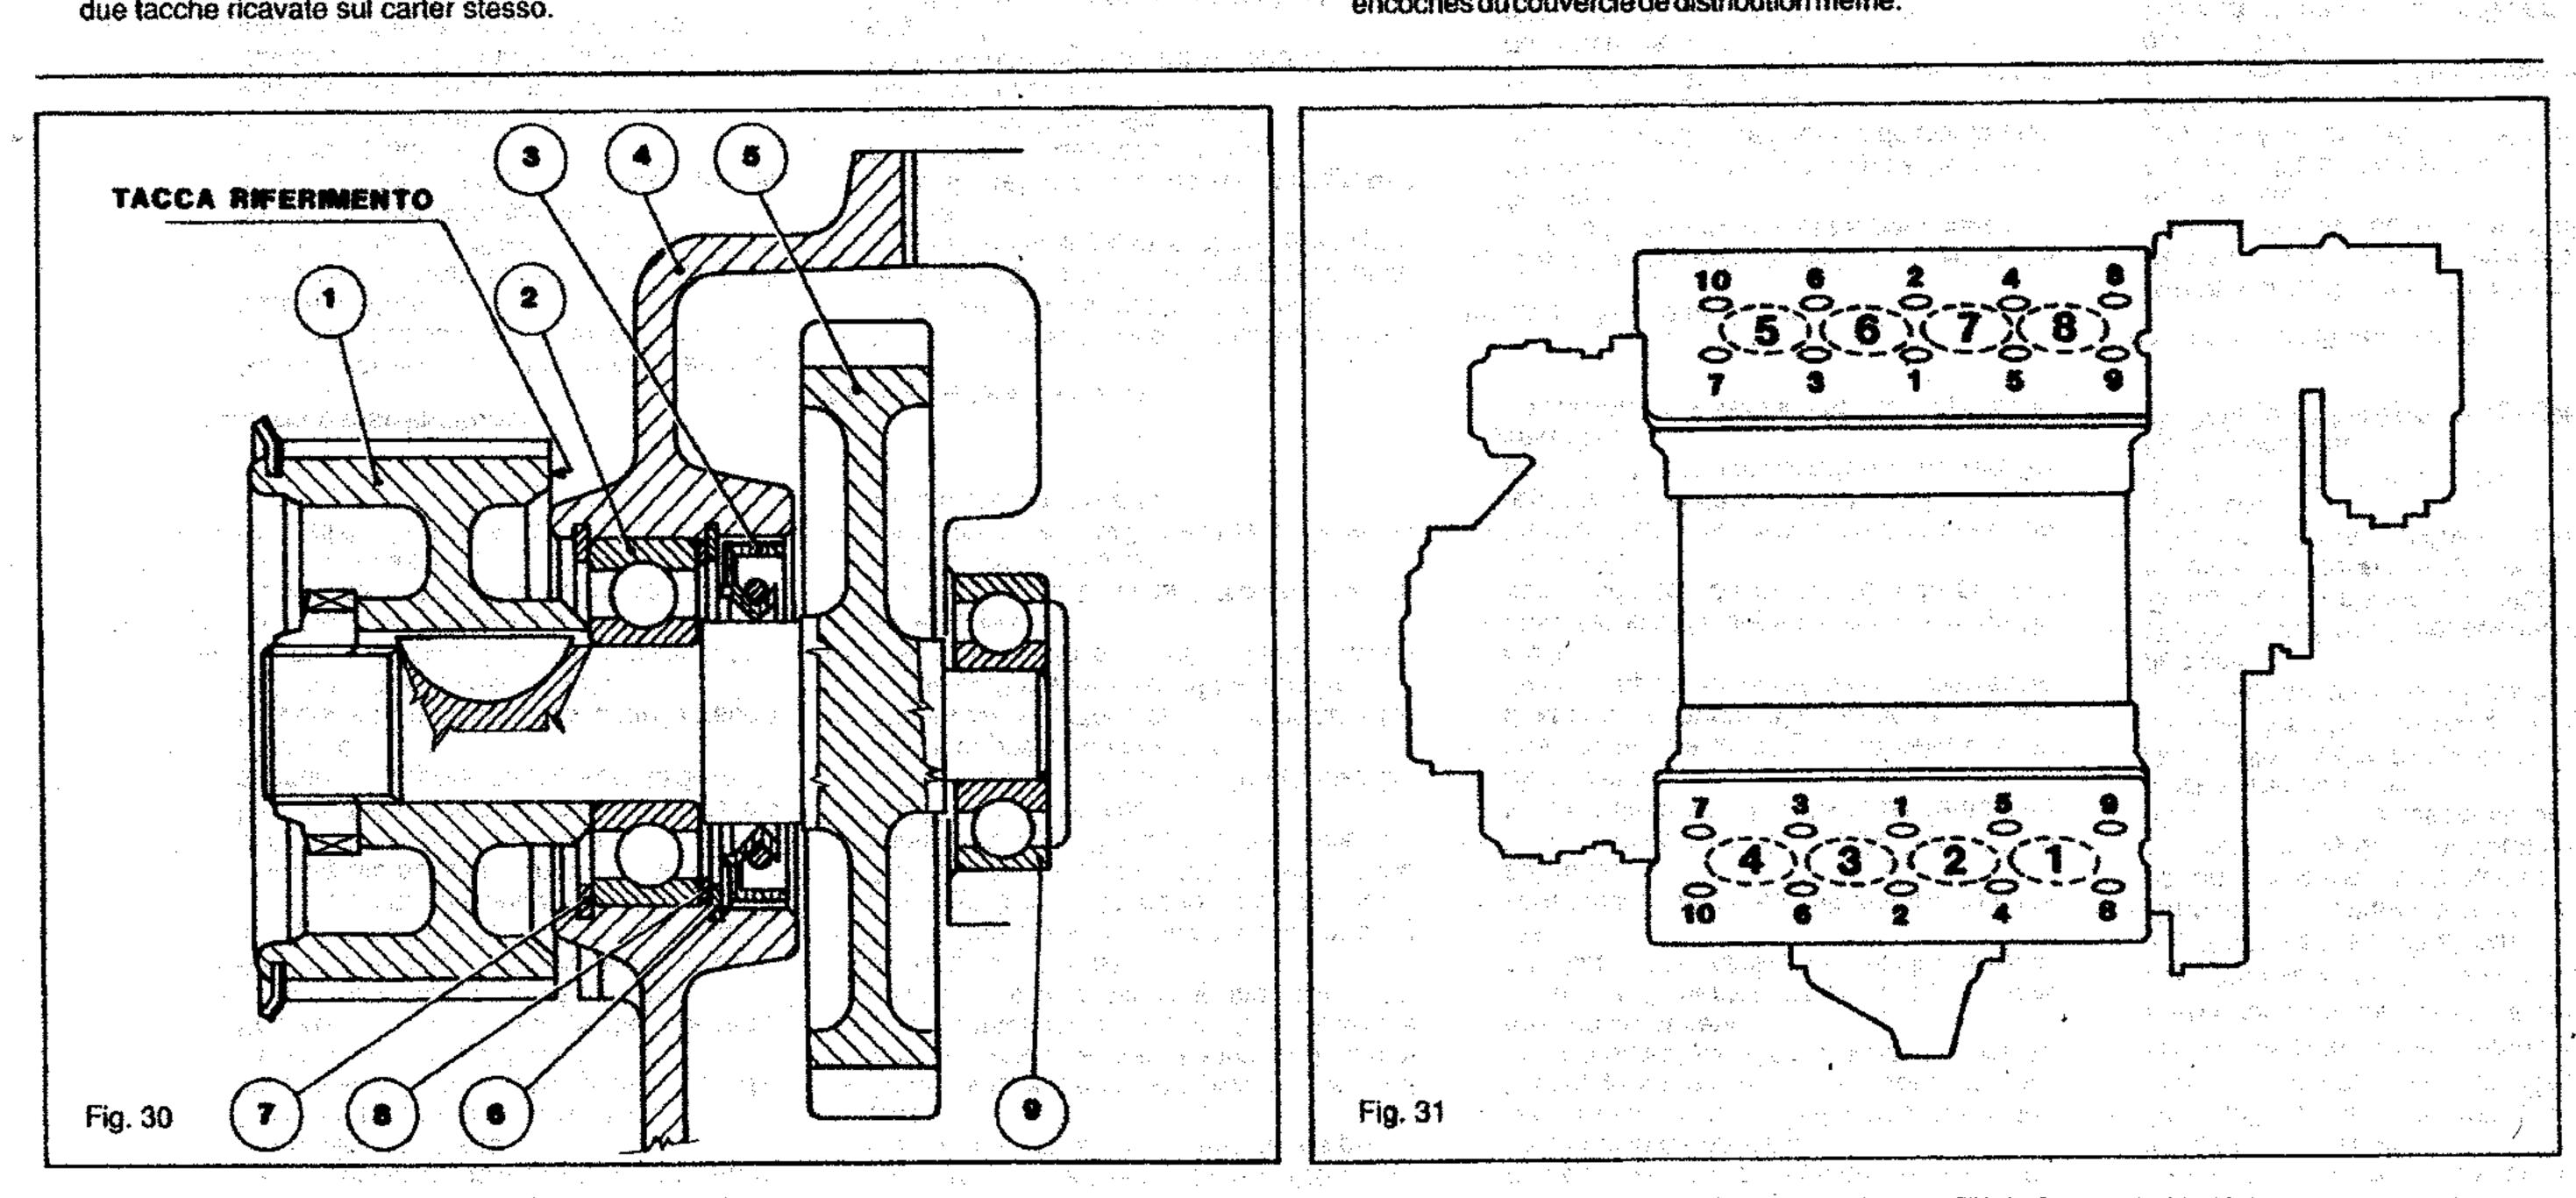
= Ingranaggi distribuzione 1 - Puleggia 2 - Cuscinetto 3 - Paraolio 4 - Carter 5 - Ingranaggio 6 - Seeger 7 - Seeger 8 - Rosetta elastica 9 - Cuscinetto Fig. 31 = Ordine chiusura dadi teste Fig. 30 = Timing system gears 1 - Pulley 2 - Bearing 3 - Oil retainer 4 - Timing case 5 - Gear 6 -Retaining ring 7 - Retaining ring 8 - Spring washer 9 - Bearing Fig. 31 = Tightening order of head nuts
